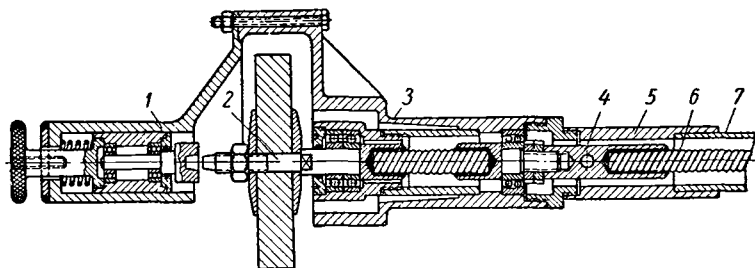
Комплектный силовой привод с малогабаритными радиально-упорными шарикоподшипниками:
